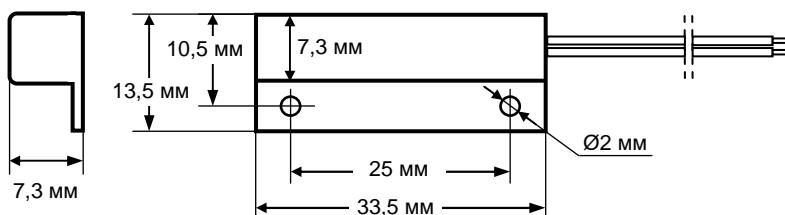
Геркон извещателя К-1 в пластмассовом корпусе
